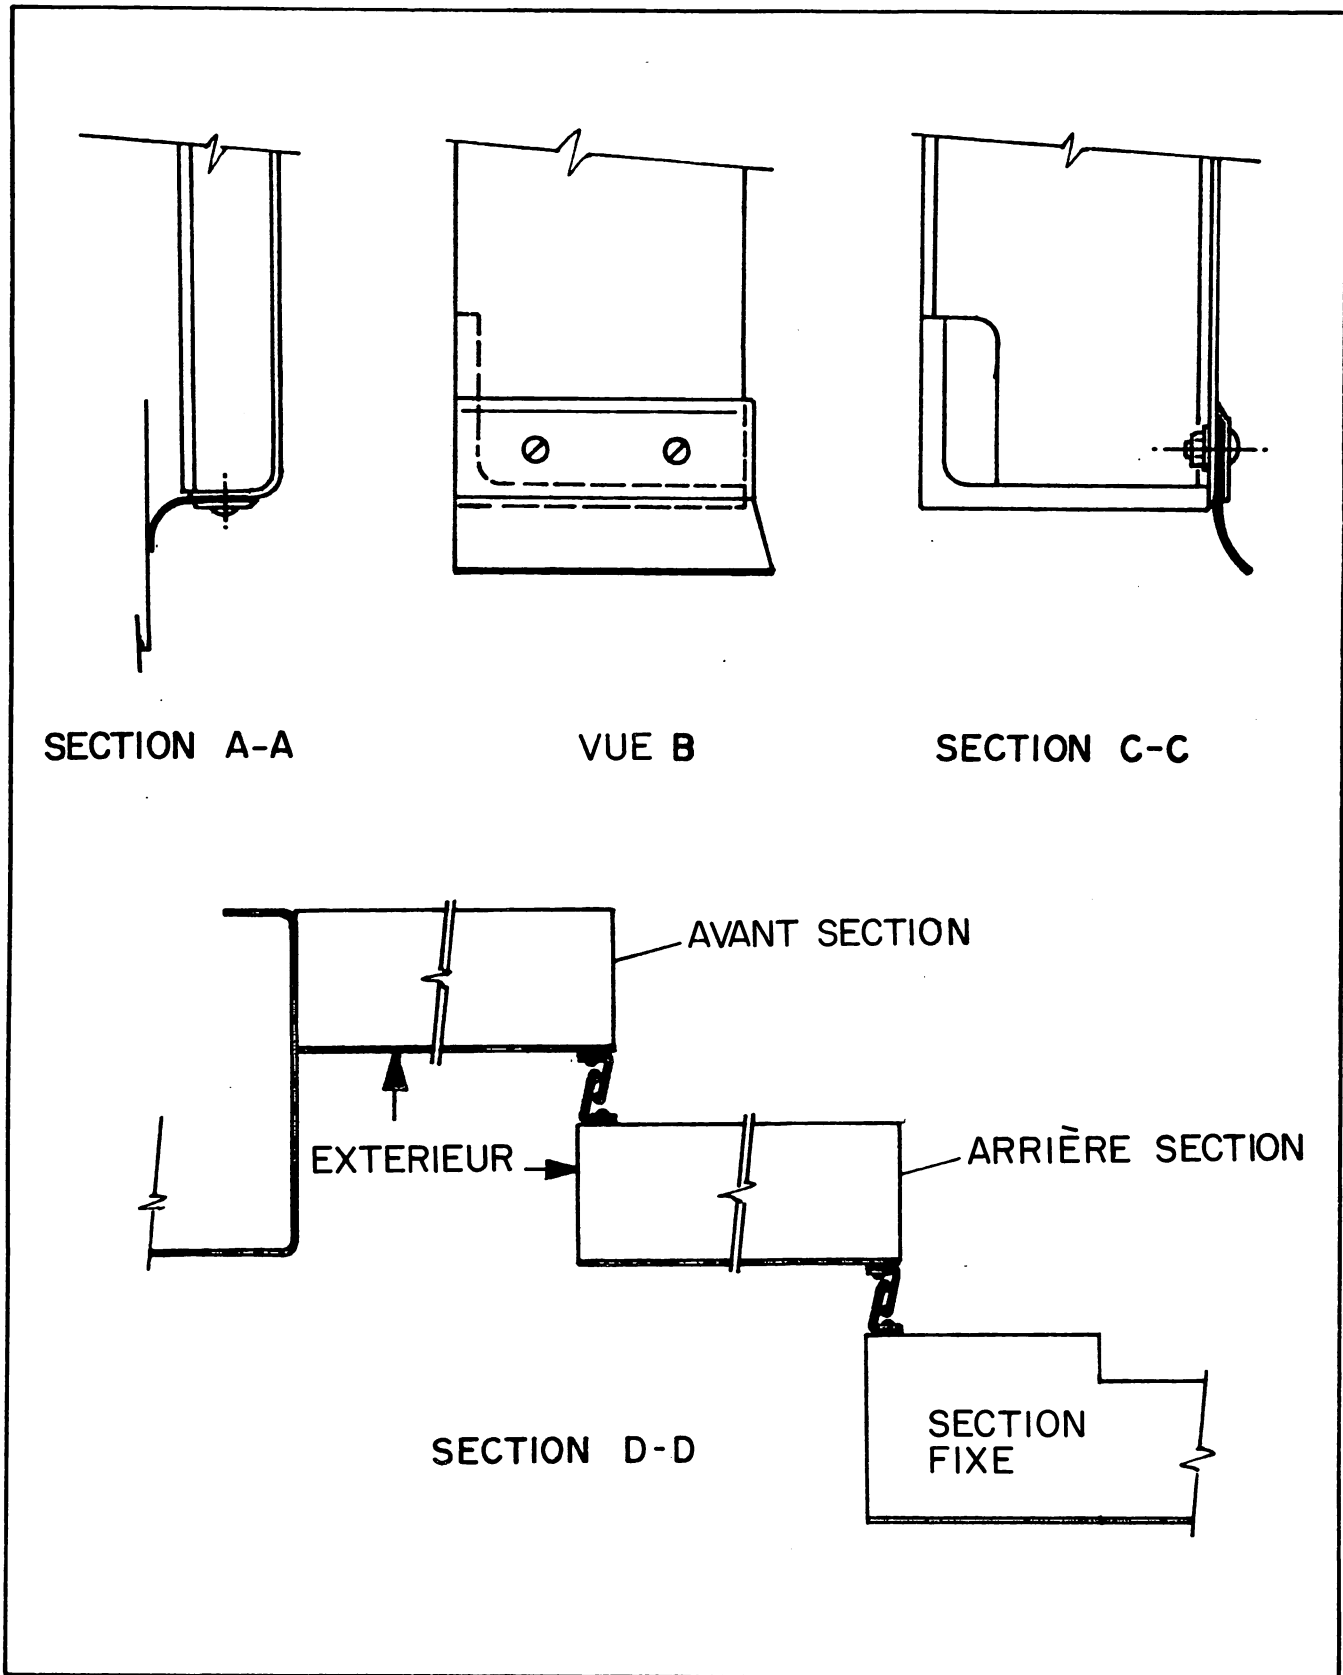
Installation des joints d'étanchéité (feuille 2 de 2)
